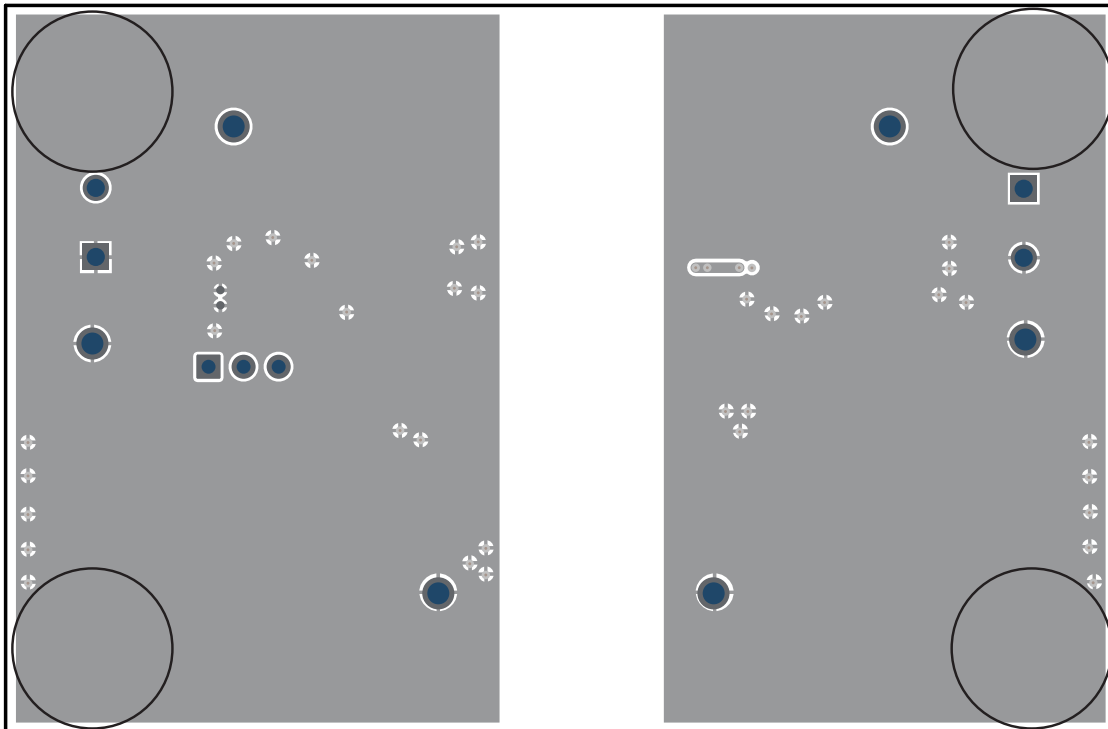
ISO7741TADWEVM PCB 布局 - 复合底视图
